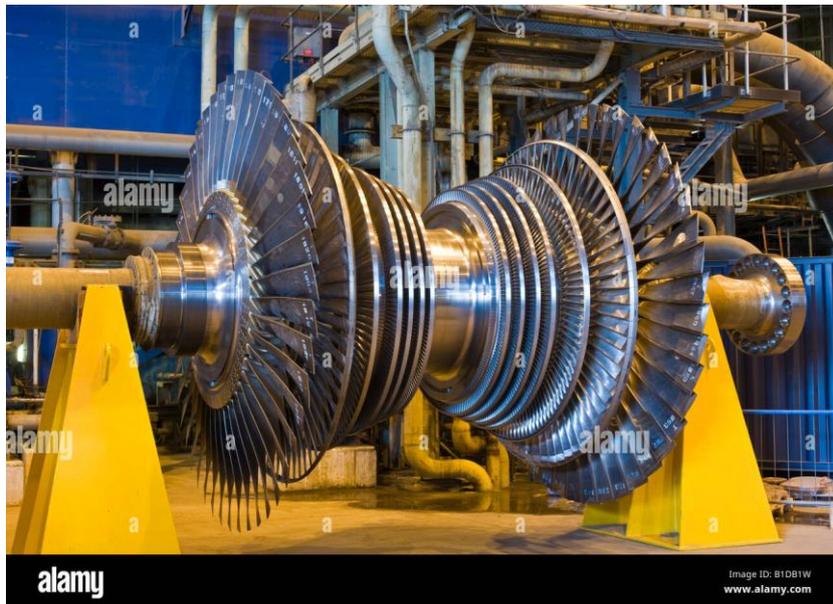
rotor BP d'une turbine à vapeur [37]
